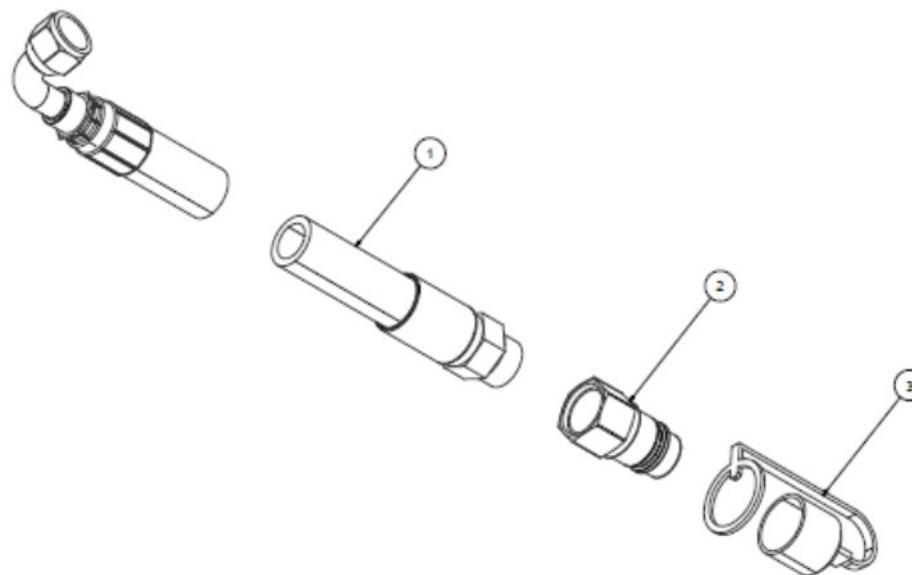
Чертеж сборки гидравлической линии – 815822
